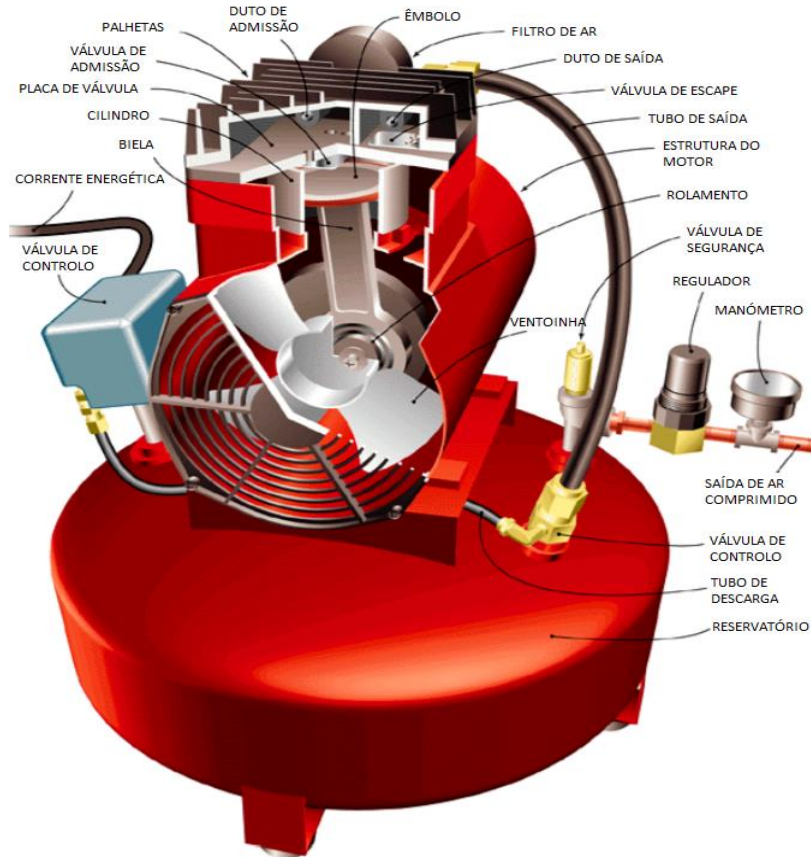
Componentes primários do compressor recíproco, adaptado de [12].
